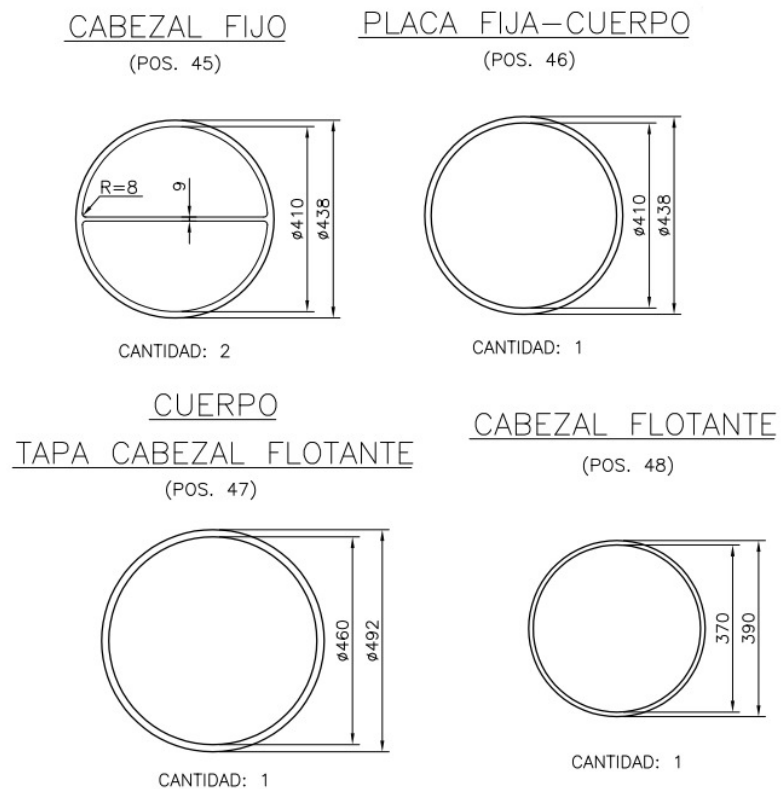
Plano de empaquetaduras enchaquetadas del 3I – 3202 / 3I – 3203
